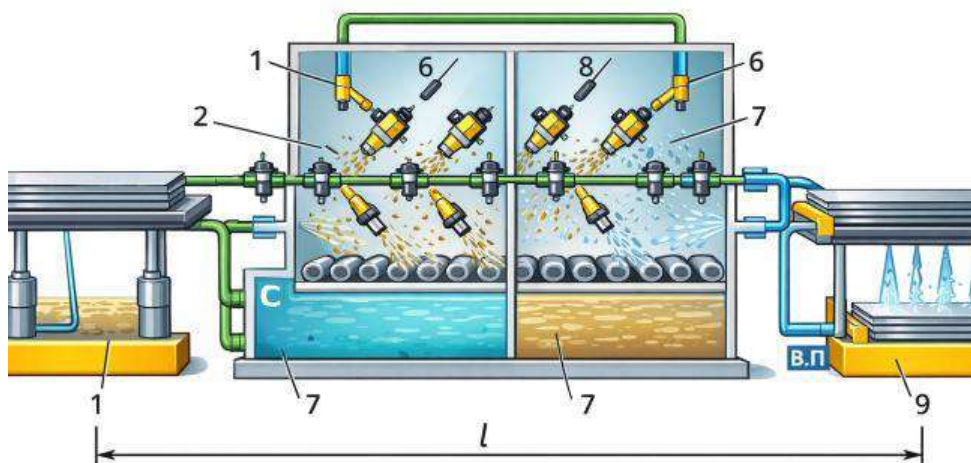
Схема розташування устаткування агрегату гідроабразивного очищення листа:
